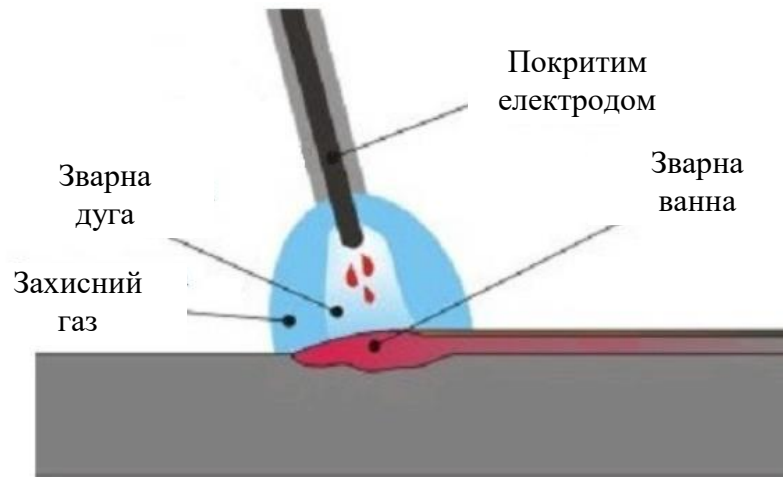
Принципова схема ручного дугового зварювання покритим електродом
